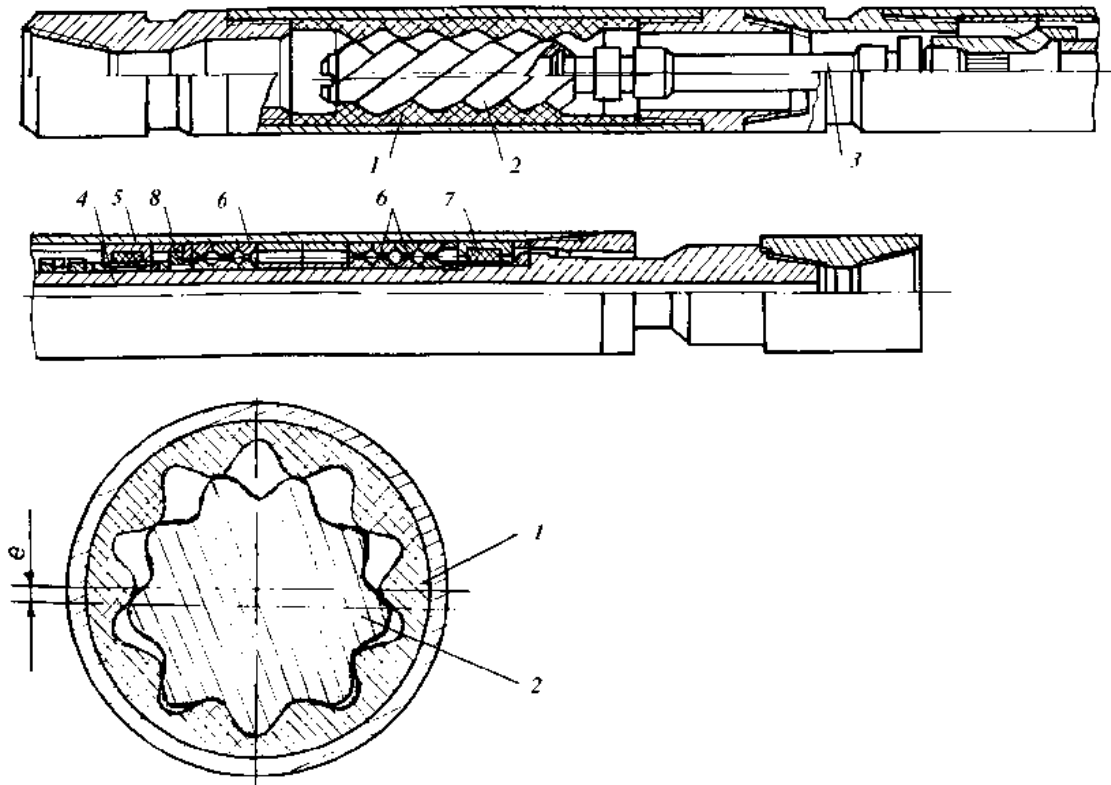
Гвинтовий вибійний двигун Д2-172:
